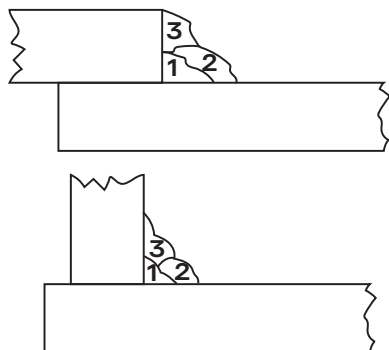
Многопроходная угловая сварка нахлесточных и тавровых соединений
